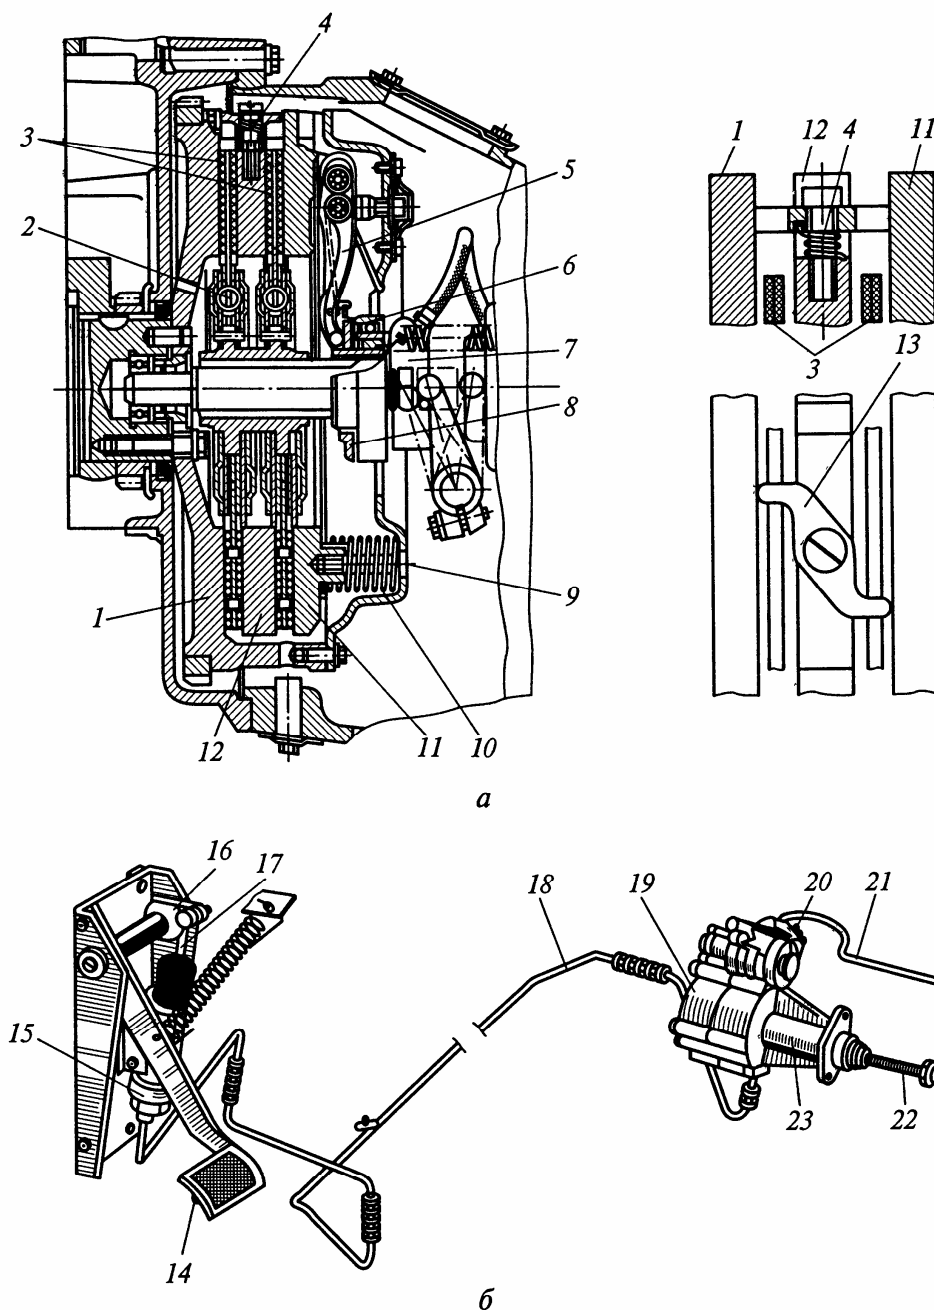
Сцепление (а) и привод (б) сцепления грузовых автомобилей КамАЗ:
